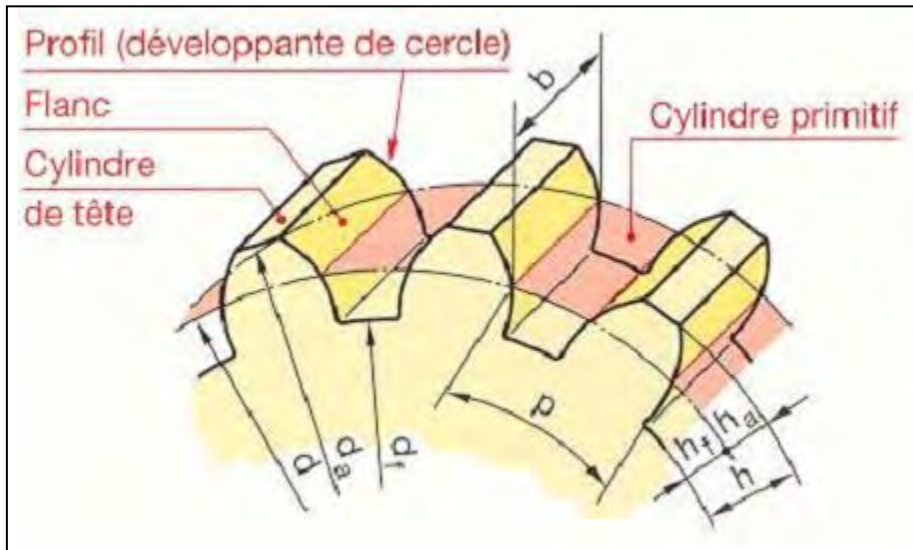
Schéma de définition d'un engrenage cylindrique
